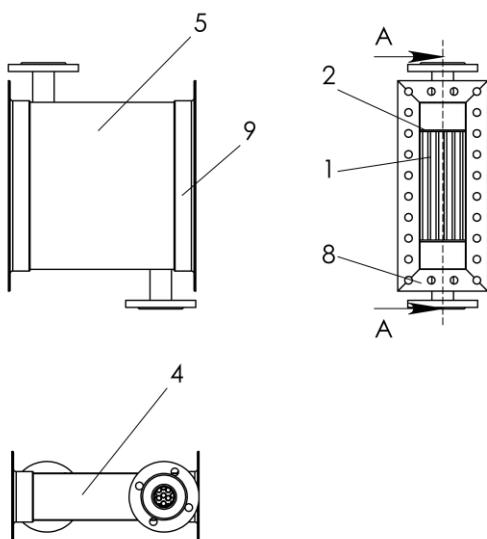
Загальний вигляд кожухотрубного теплообмінника
